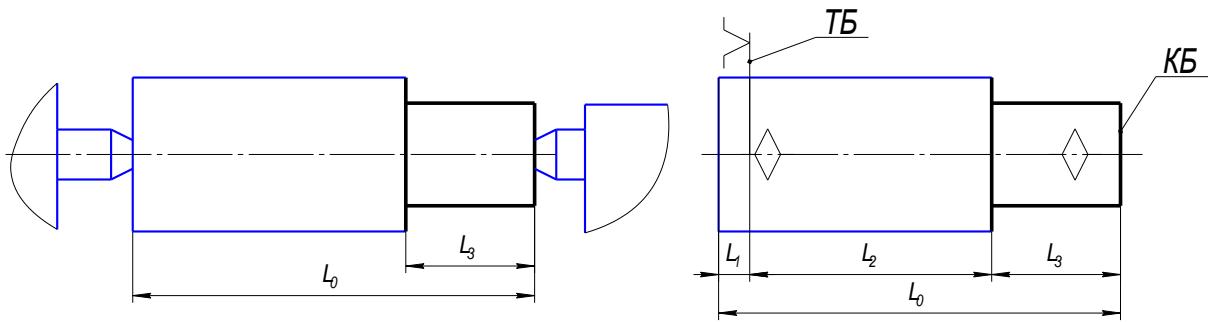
Розмірна схема операції обробки шийки вала для визначення похибки базування
